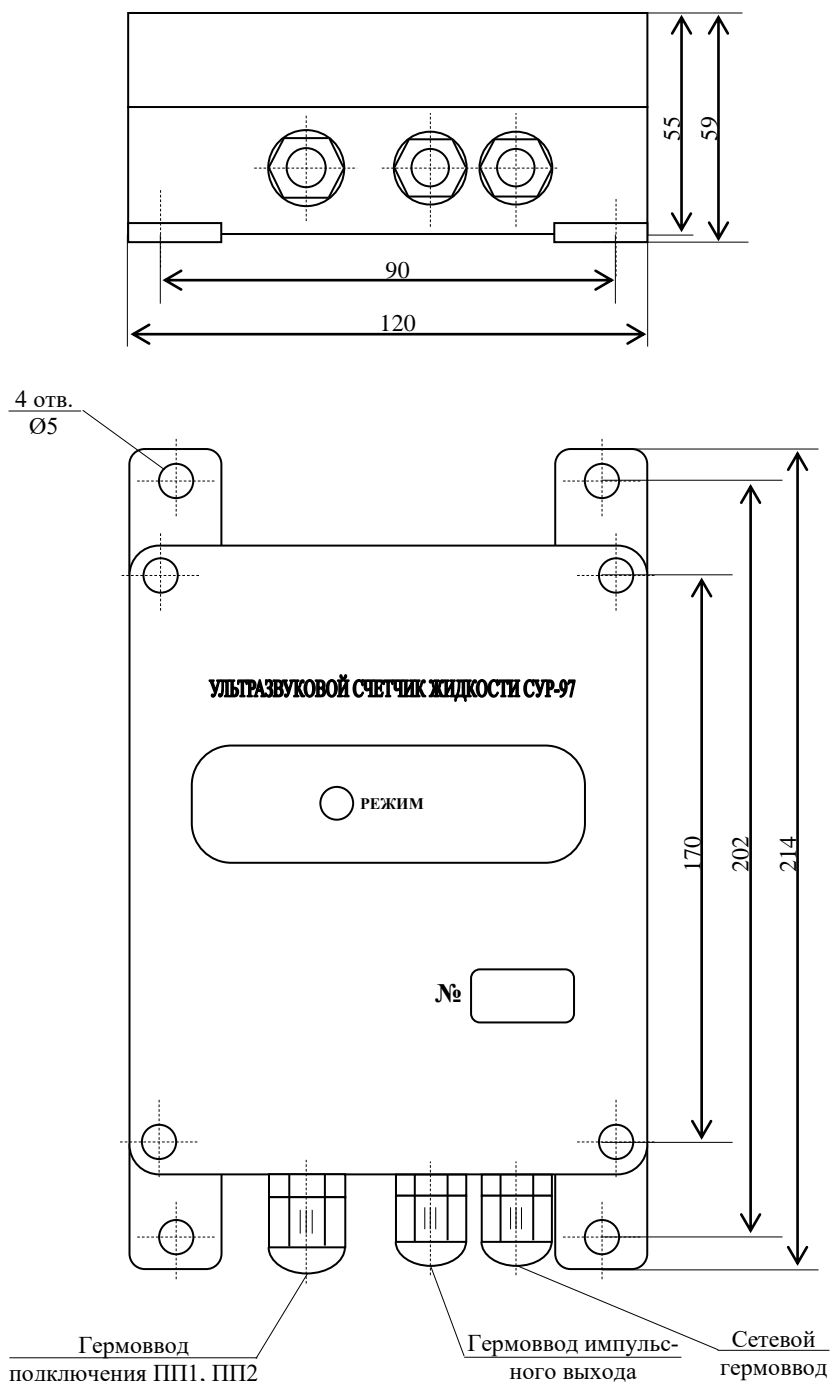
б - Внешний вид ЭП без индикации (габариты, установочные размеры)
